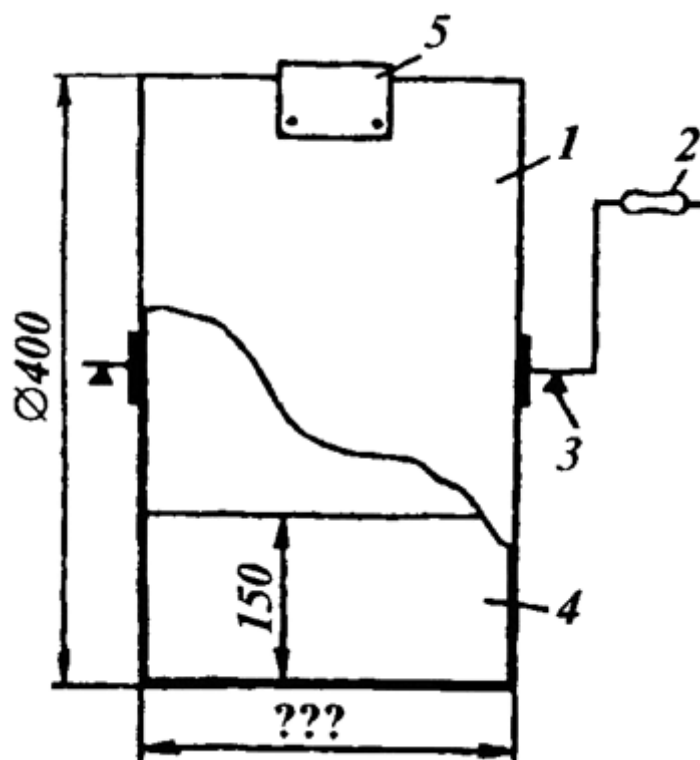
Барабан для выделки кожи: 1 - корпус, 2 - привод ручной или через электрический редуктор, 3 - подшипник, 4 - лопасть, 5 - крышка люка
